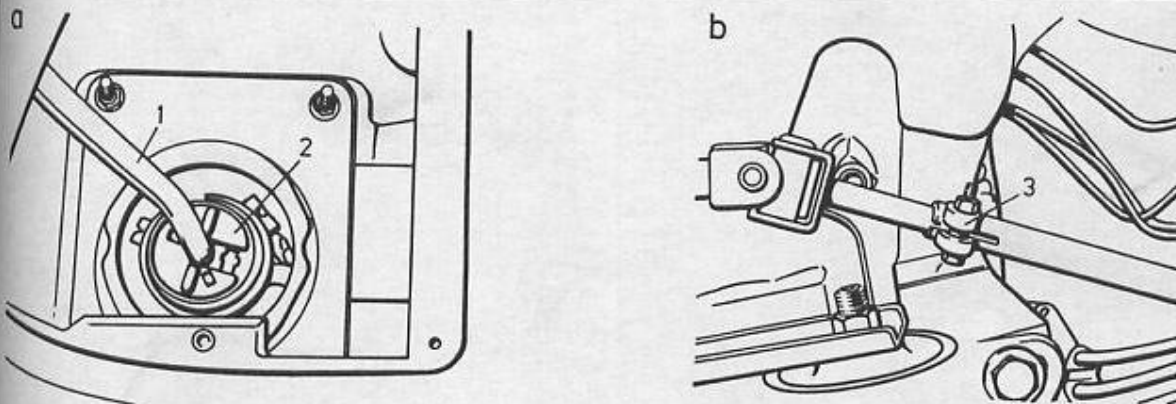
PRZYRZĄD 16-057 DO WYMONTOWANIA
